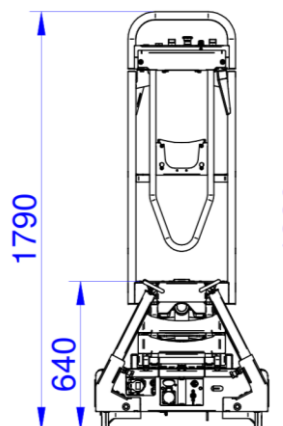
; Dimensions de la hauteur minimale en mm, 3 pantographes
